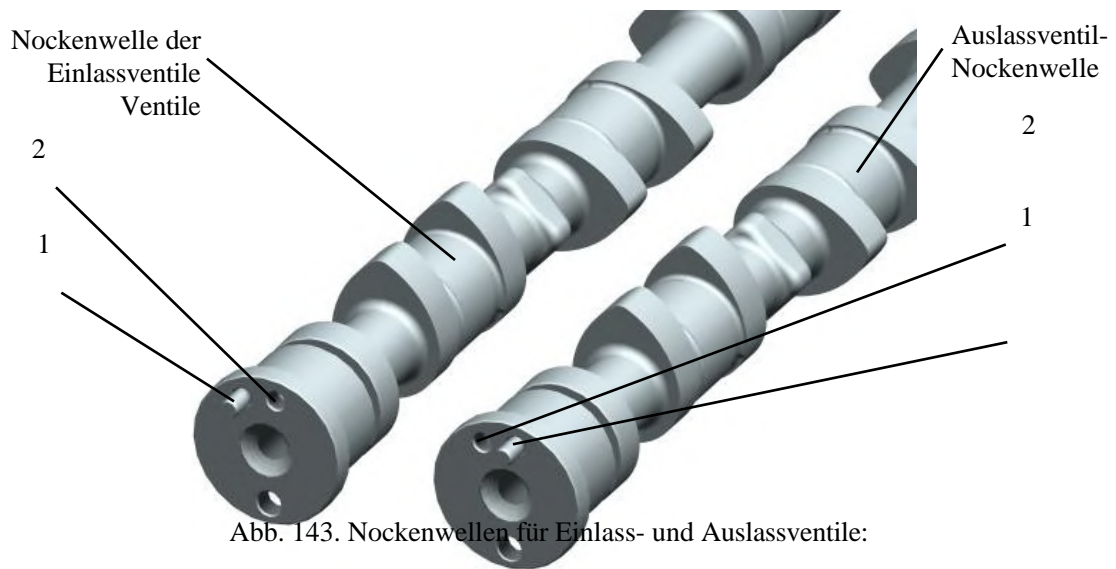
Nockenwellen für Einlass- und Auslassventile:
